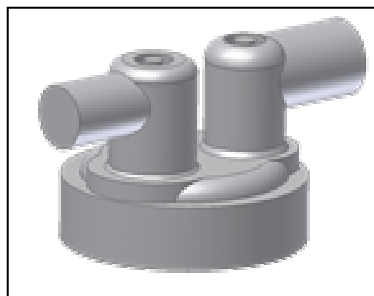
Fluid que omple les cavitats de la culata del motor Honda Gx35.
